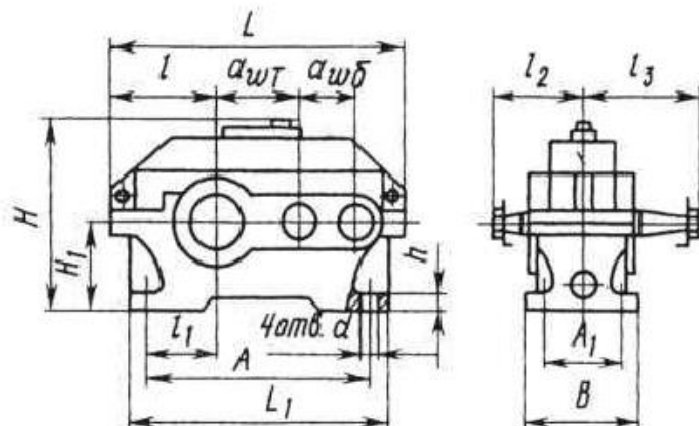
Схема сборки цилиндрического двухступенчатого редуктора (ГОСТ 20373-94)
